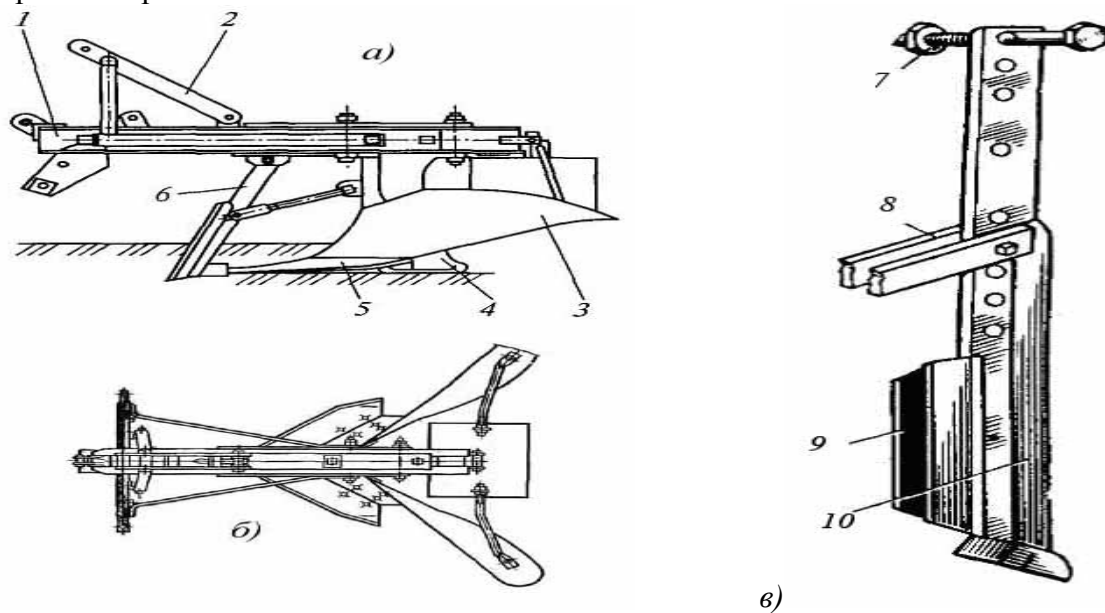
Плуг ПКЛ-70 (двухотвальный корпус) с установленным черенковым ножом: а) вид сбоку: 1 — рама; 2 — навесное устройство; 3 — корпус плуга; 4 — опорная пята; 5 — лемех; 6 — черенковый нож; б) вид сверху; в) черенковый нож с прямым резцом: 7 — болт специальный, 8 — тяга, 9 — направляющая резца, 10 — резец с долотом
